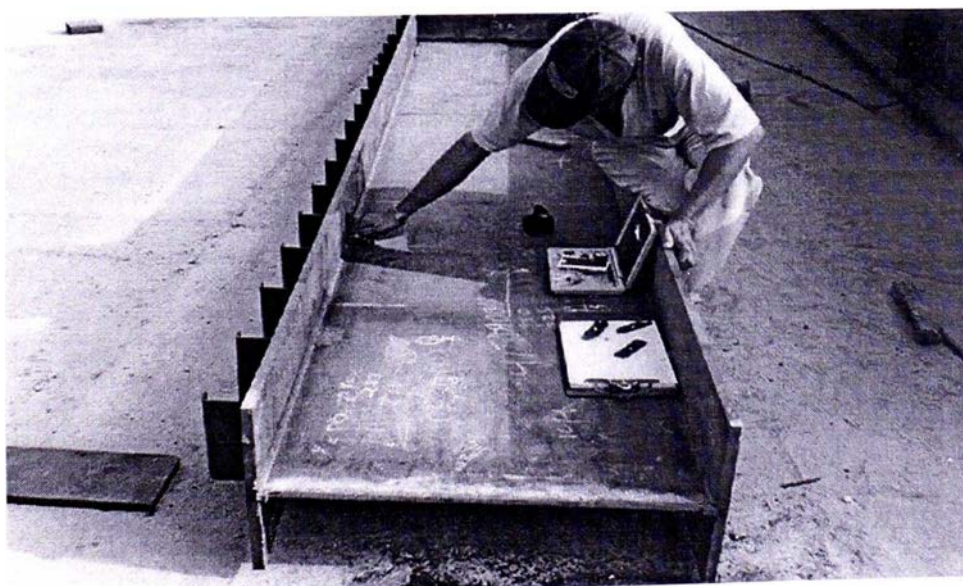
Inspección Visual – Verificación del Tamaño de una Soldadura de Filete.
